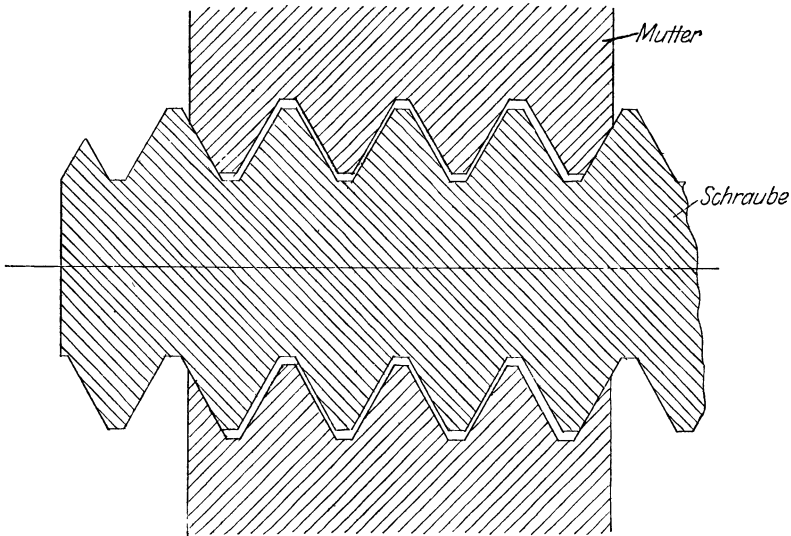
Die Steigung der Schraube ist zu kurz.
